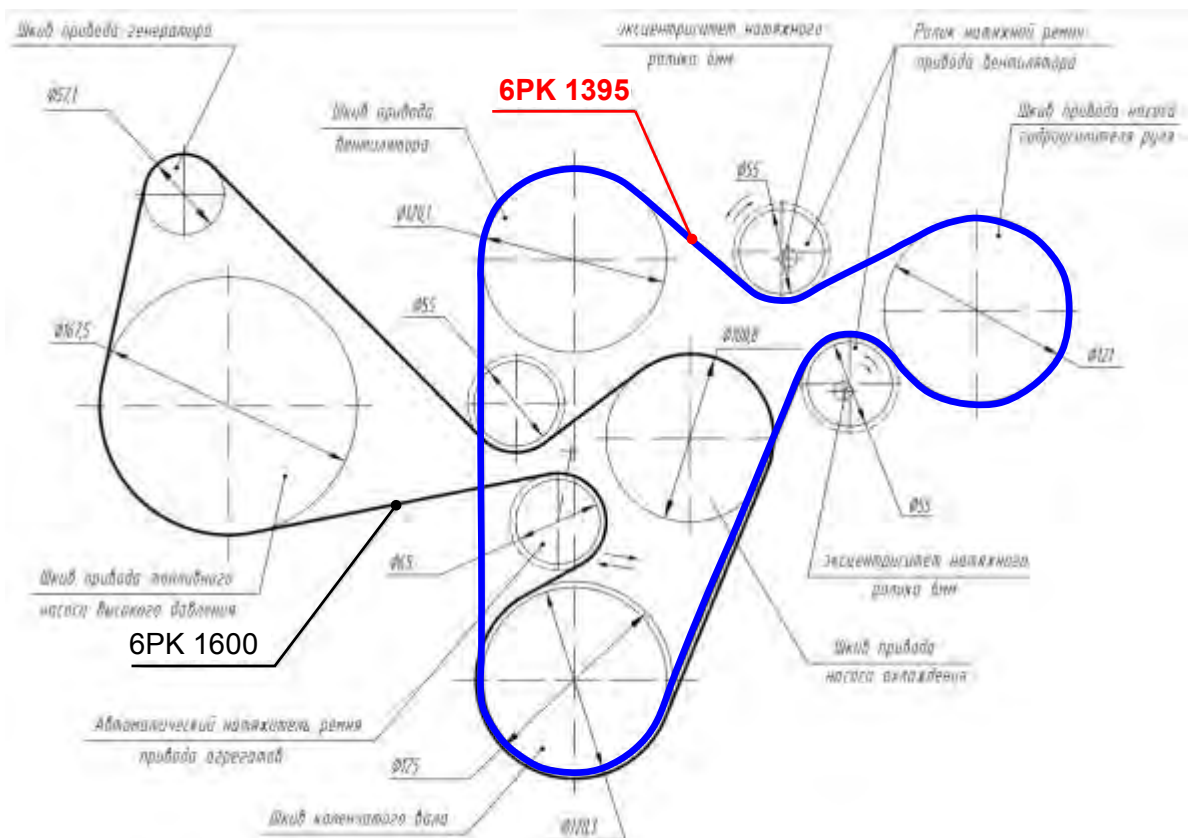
Схема привода вспомогательных агрегатов двигателя для автомобилей на платформе УАЗ-3163 без компрессора кондиционера
